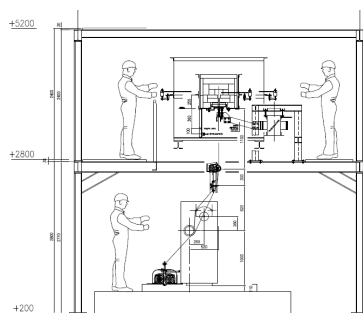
Immagini dal progetto dell'impianto pilota per la produzione di fibre di basalto
